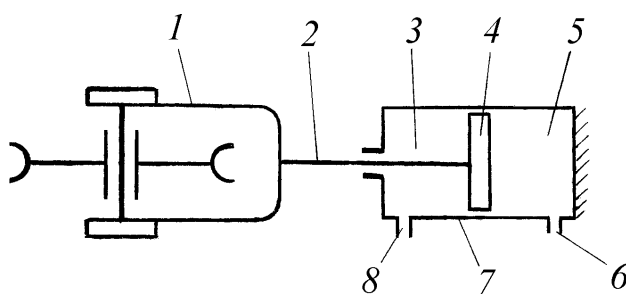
Схема конструкции пневмогидравлического натяжного и амортизирующего устройств
